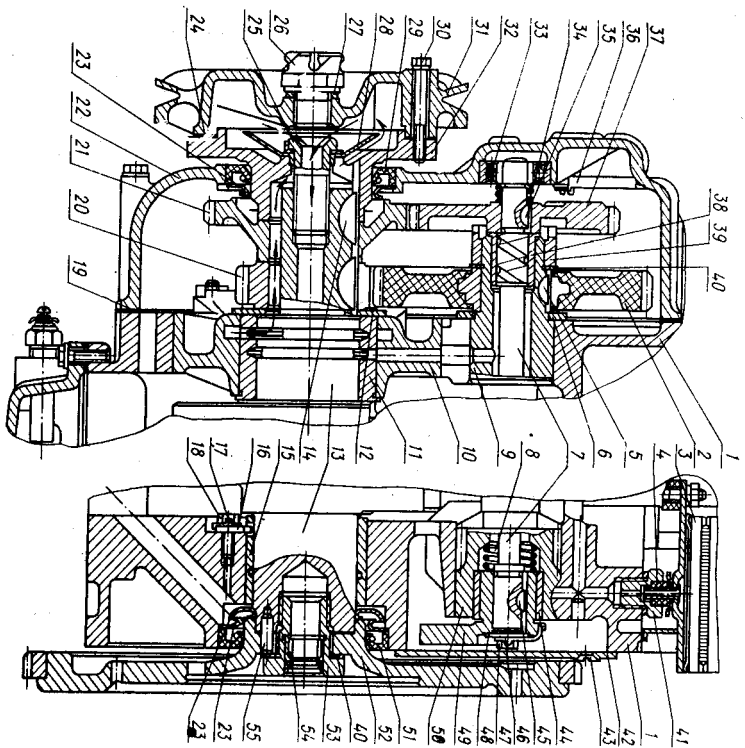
Привод распределительного вала, балансирного механизма и задний коренной подшипник.
